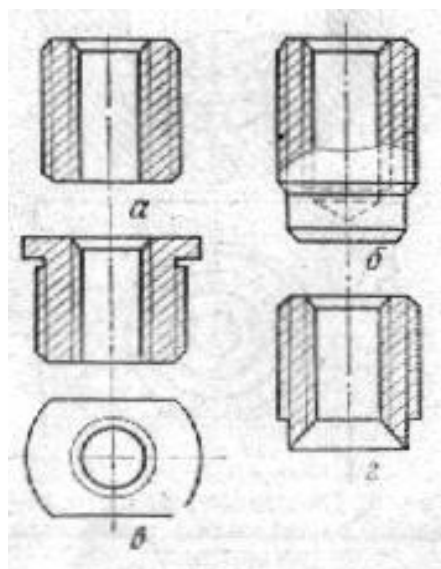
Основные типы свертышей: а – прямой открытый; б – прямой закрытый; в – прямой открытый с буртиком под ключ; г – ступенчатый
